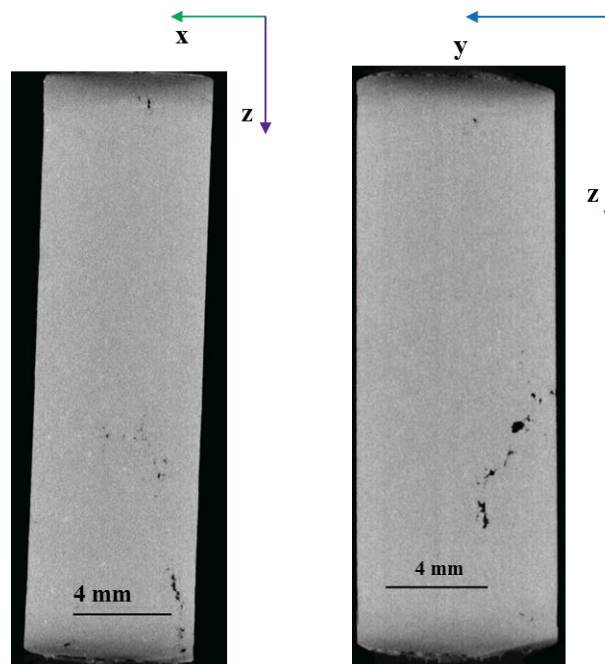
Coupes représentant les retassures internes de la pièce comprimée à chaud. A gauche sur le plan xOz et à droite sur le plan yOz
